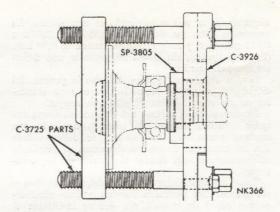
Colocación de un rodamiento y collarin nuevos en un semieje trasero. («Parts» = piezas).
